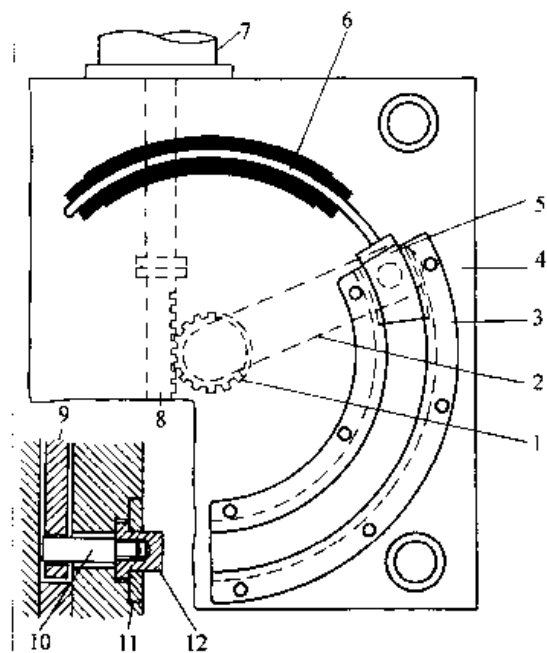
液压缸带动齿条齿轮传动的回转型芯
